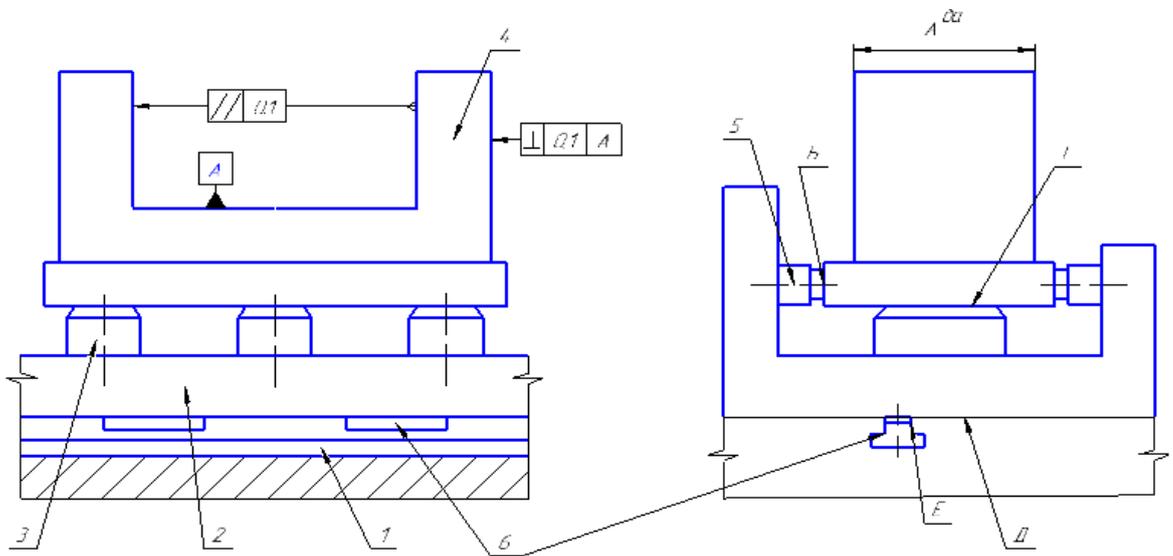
Схема установки заготовки в приспособлении при фрезировании
